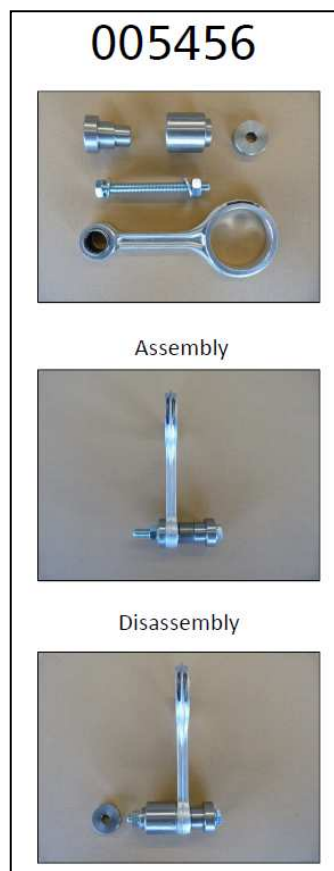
L&W Pleuellager Montagewerkzeug 005456
